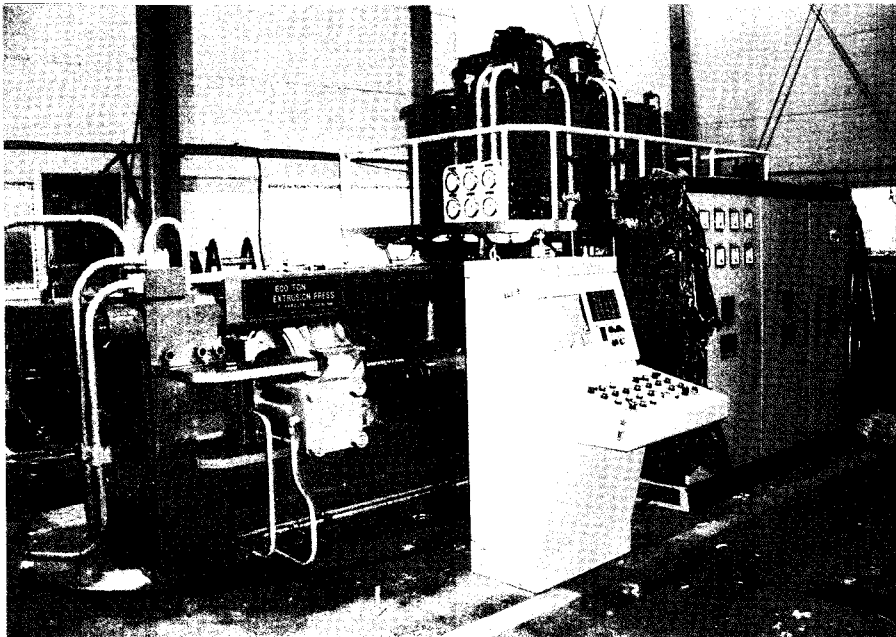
개발된 CNC 제어 가변단면 압출시스템
